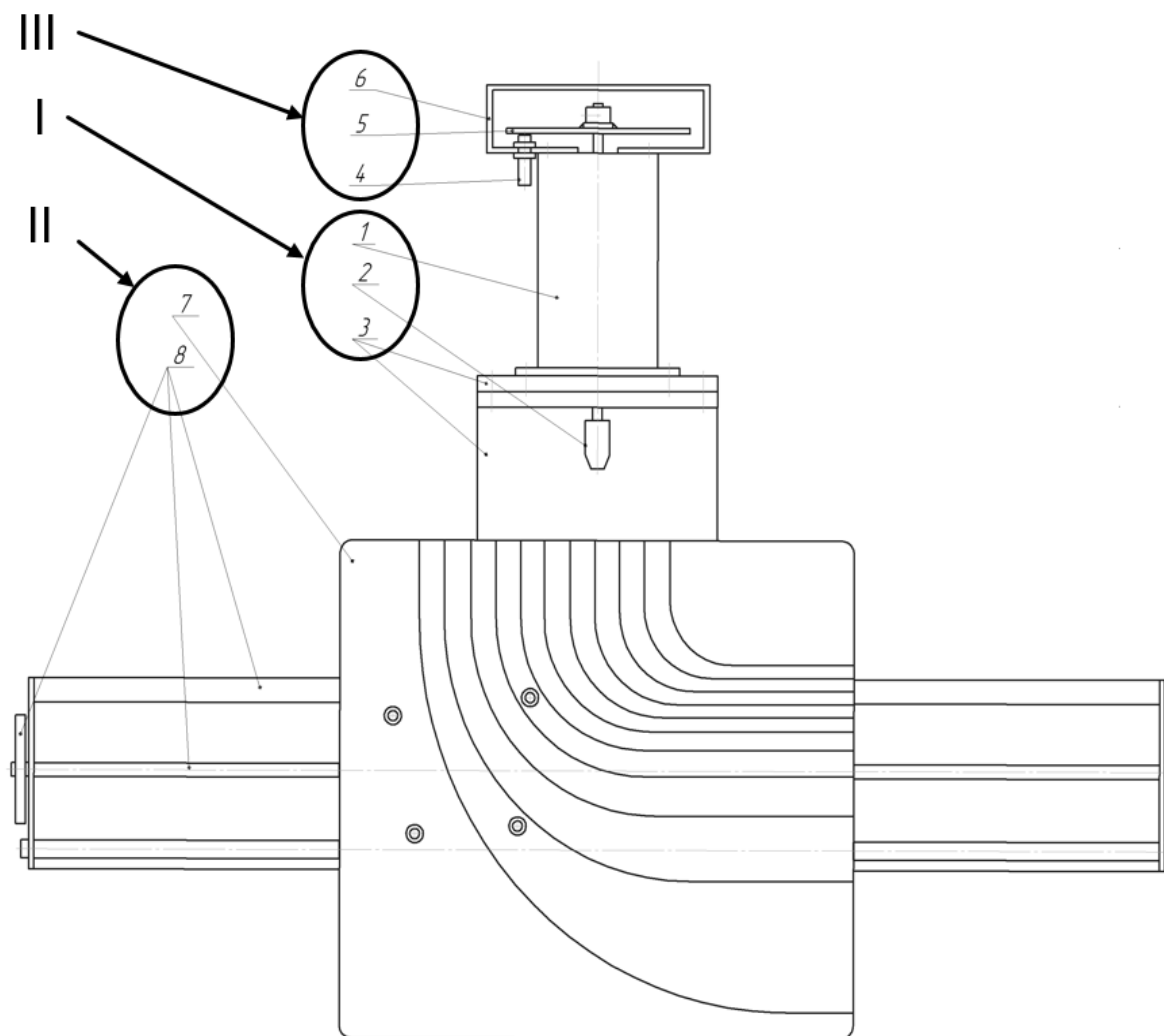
Схема спроектированной установки для усталостных испытаний проволоки
